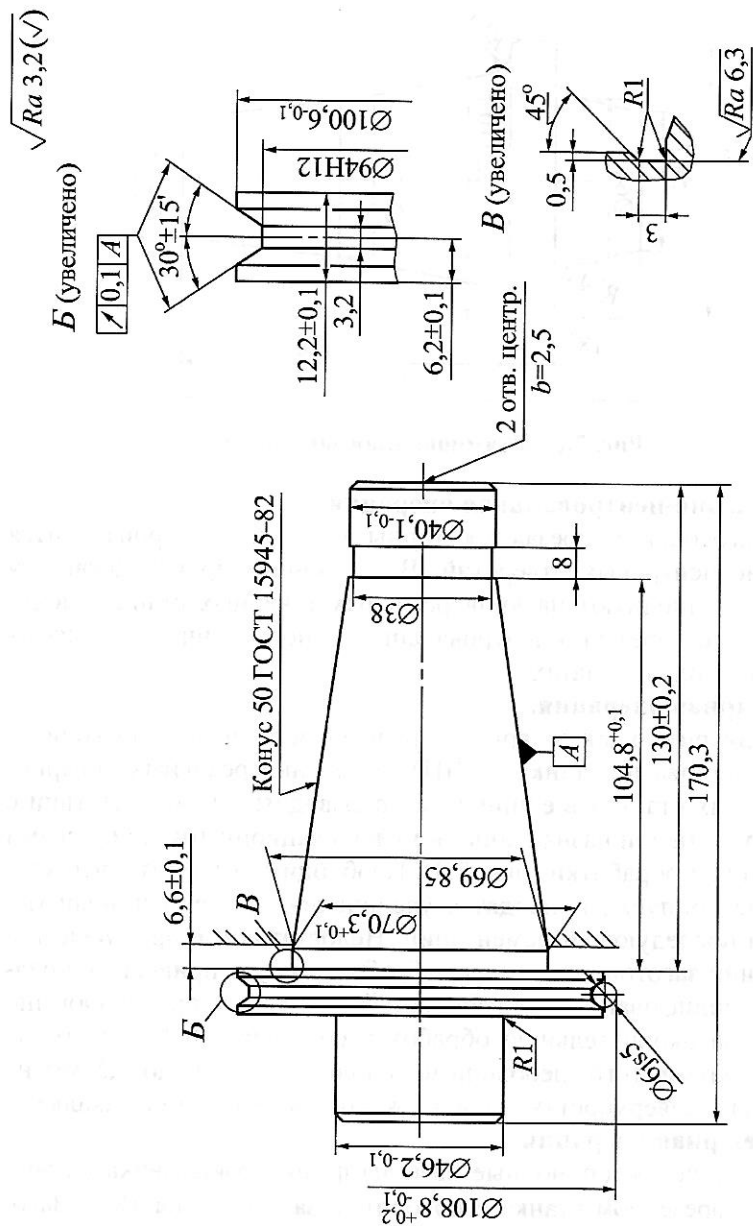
Эскиз заготовки корпуса ВИ с конусом 7:24 после токарной обработки
